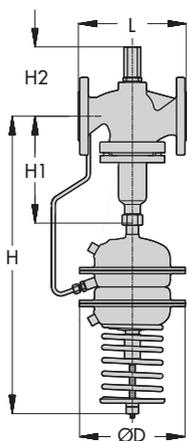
Dimensioni, valvola Tipo 2423 , con membrana di bilanciamento
